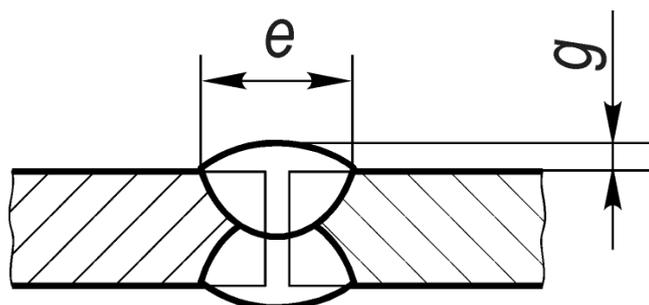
Схема сварочного шва С7 согласно ГОСТ 14771-76
